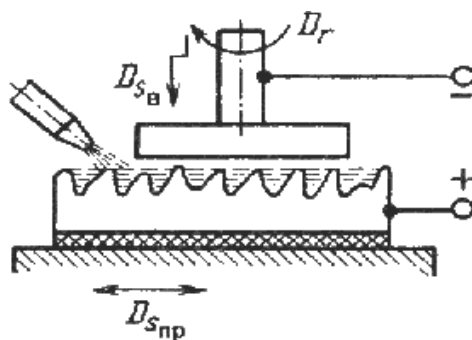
Схема анодно-механічної обробки плоскої поверхні.
